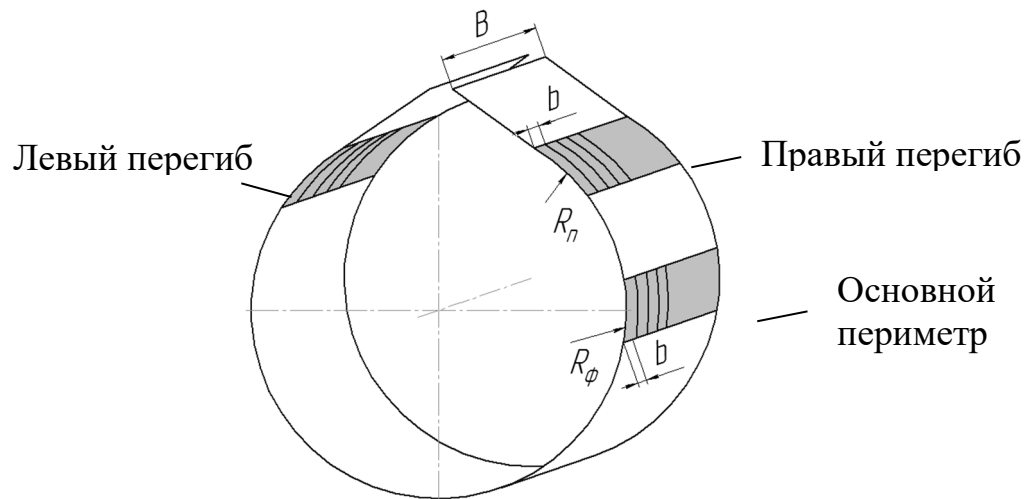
Схема вырезки образцов от кольца после формовки
